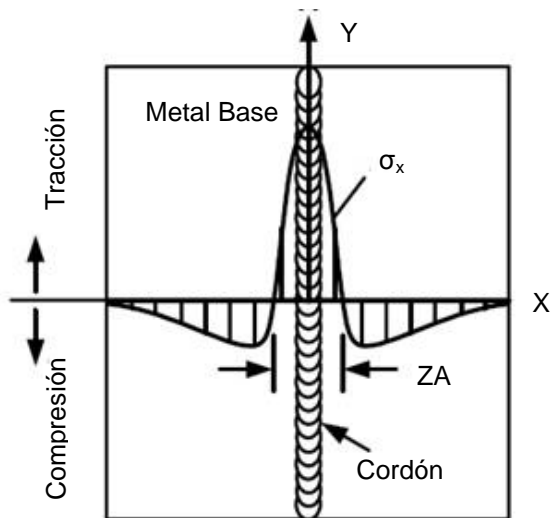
Distribución de esfuerzos residuales en una junta soldada [8].
